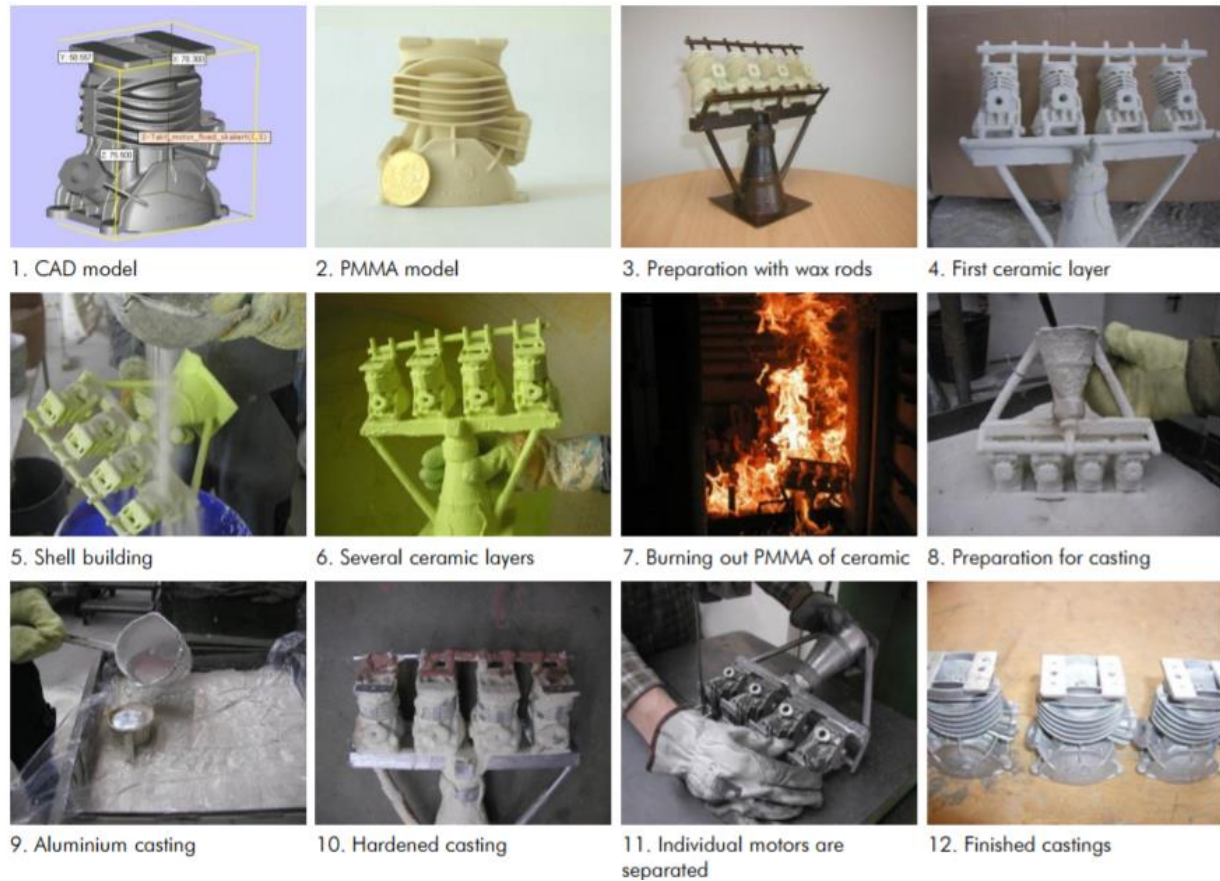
Proceso de fabricación de una pieza metálica mediante la impresión de una pieza plástica. (Voxeljet)
